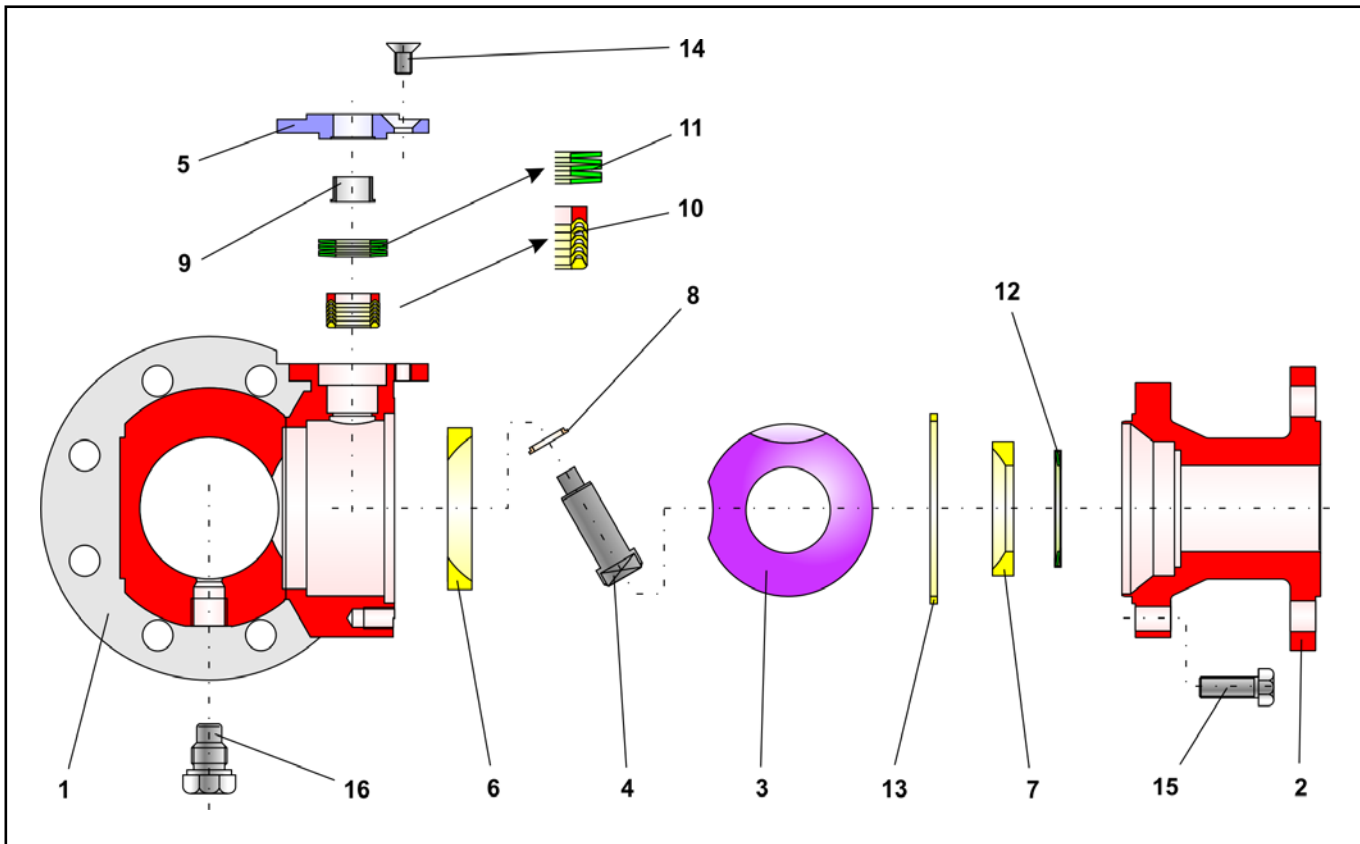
Explosionszeichnung der Eindosierung BR 28a
